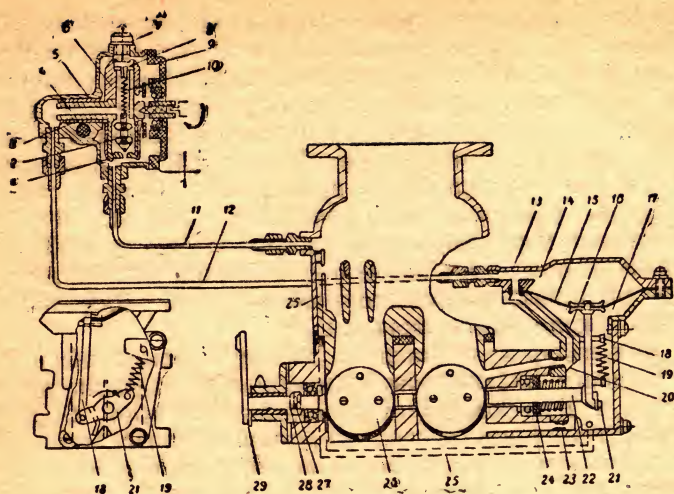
Ограничитель максимального числа оборотов коленчатого вала двигателя ЗИЛ-130
